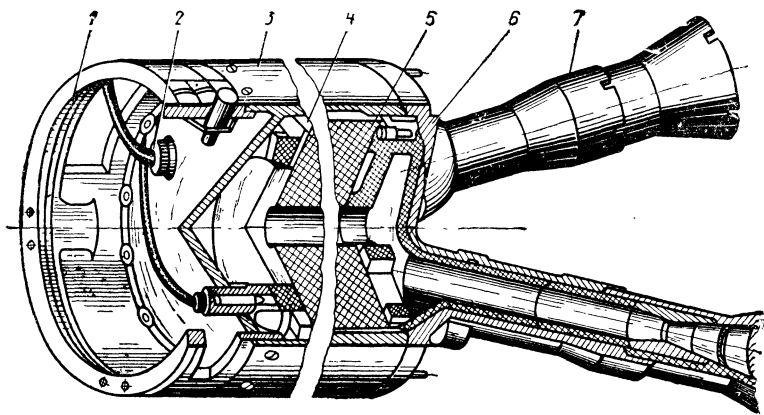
Двухсопловый ракетный двигатель твердого топлива:
